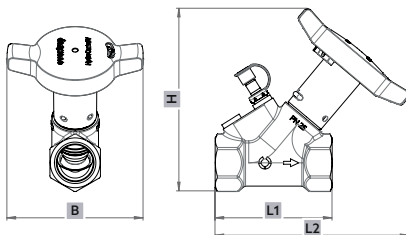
Abmessungen Seitenansicht / Frontansicht Innengewinde
